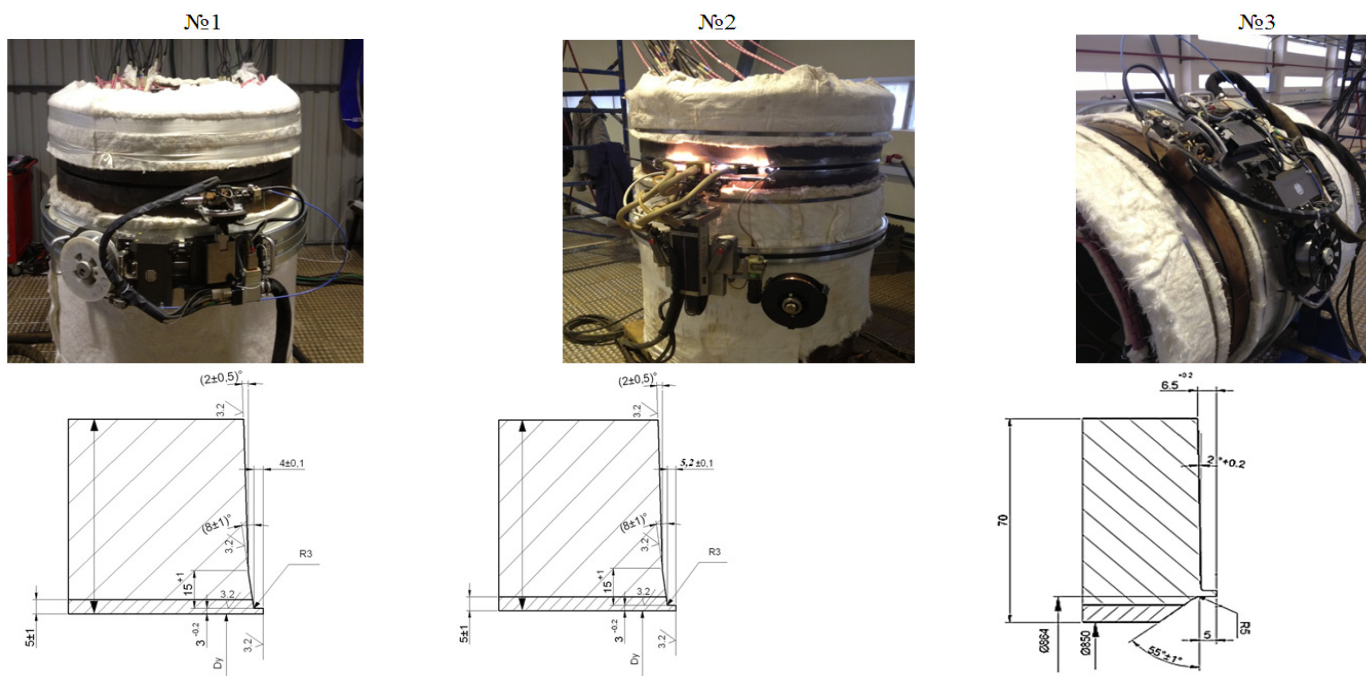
Подготовка кромок и сварка натуральных макетов в узкощелевую разделку биметаллического трубопровода Ду850.
